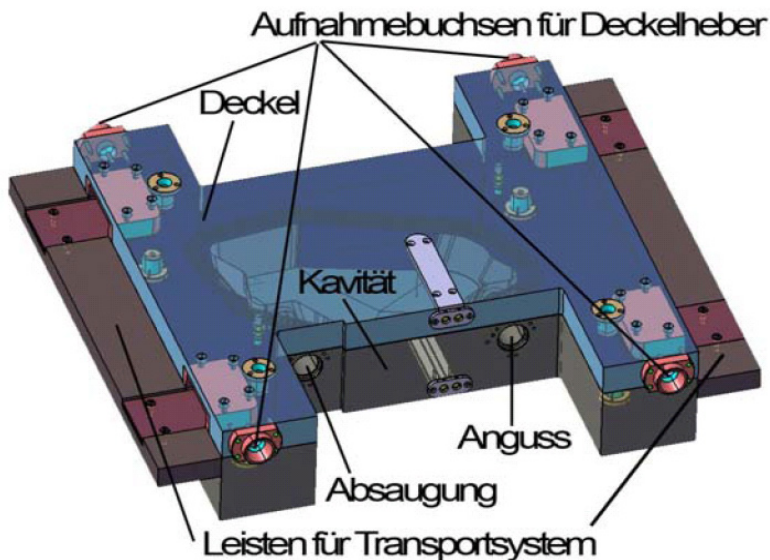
Auto-RTM-Werkzeugkonzept /14/
